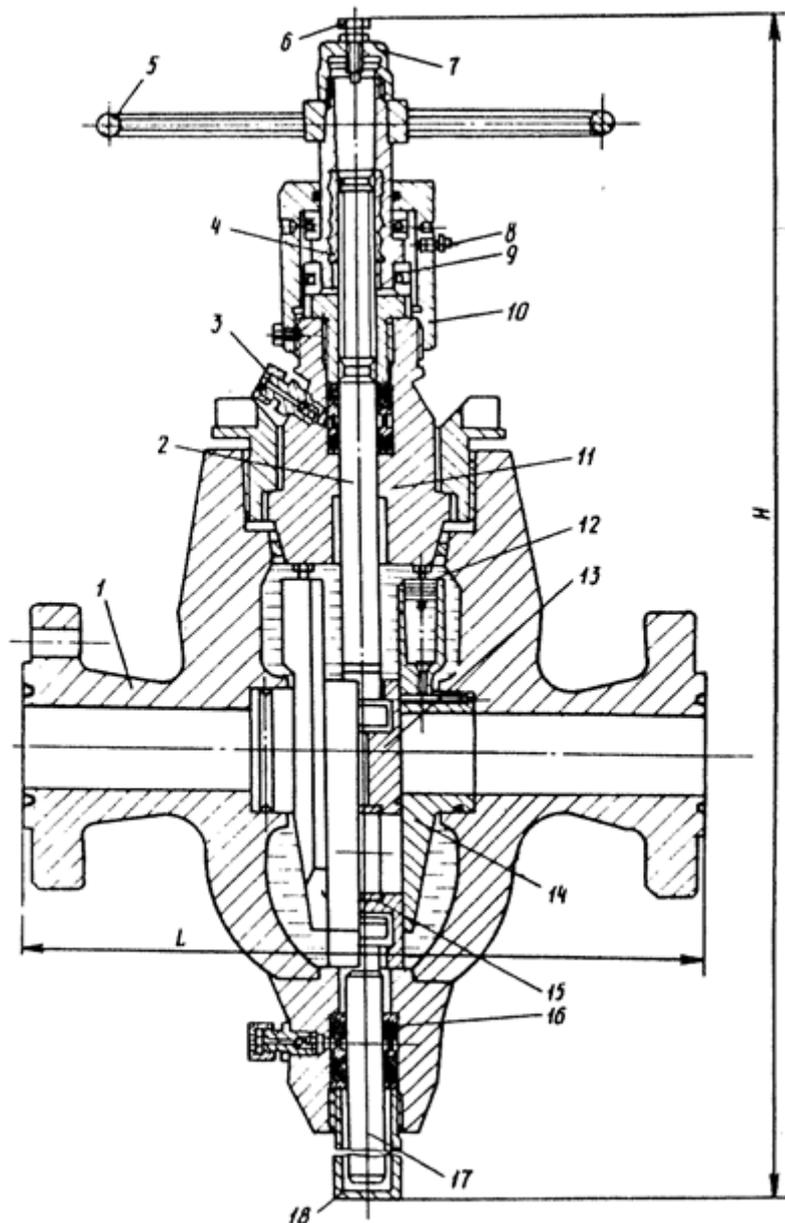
Задвижка типа ЗМАД с ручным приводом:
